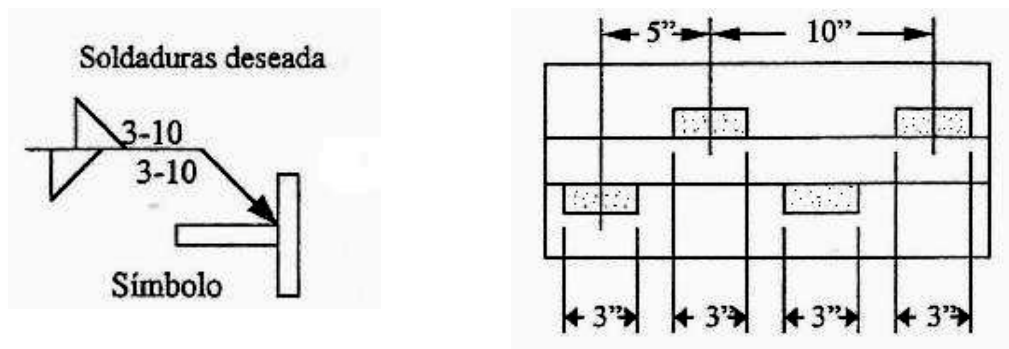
SOLDADURAS DE FILETE INTERMITENTE ALTERNADAS.
